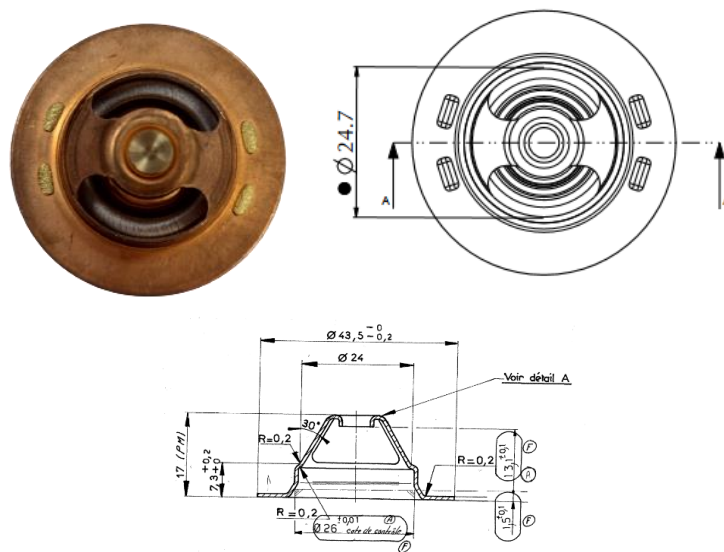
Base del termostato de muestra y plano de la base disponible en planta
